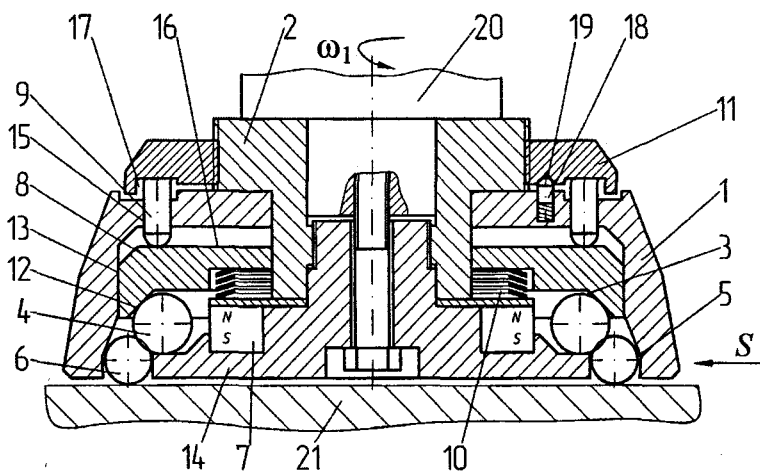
Инструмент для МДН плоских поверхностей с устройством регулирования натяга между деформирующими и приводными шарами
